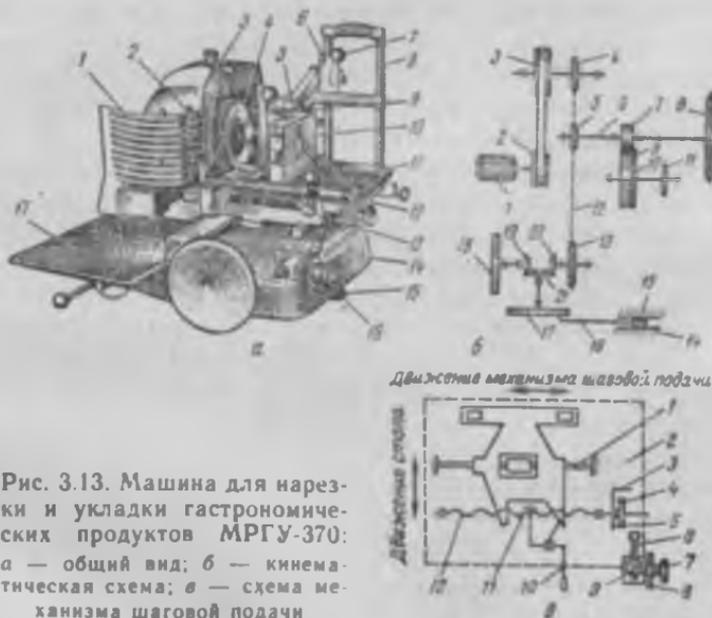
Машина для нарезки и укладки гастрономических продуктов МРГУ-370: а — общий вид; б — кинематическая схема; в — схема механизма шаговой подачи
